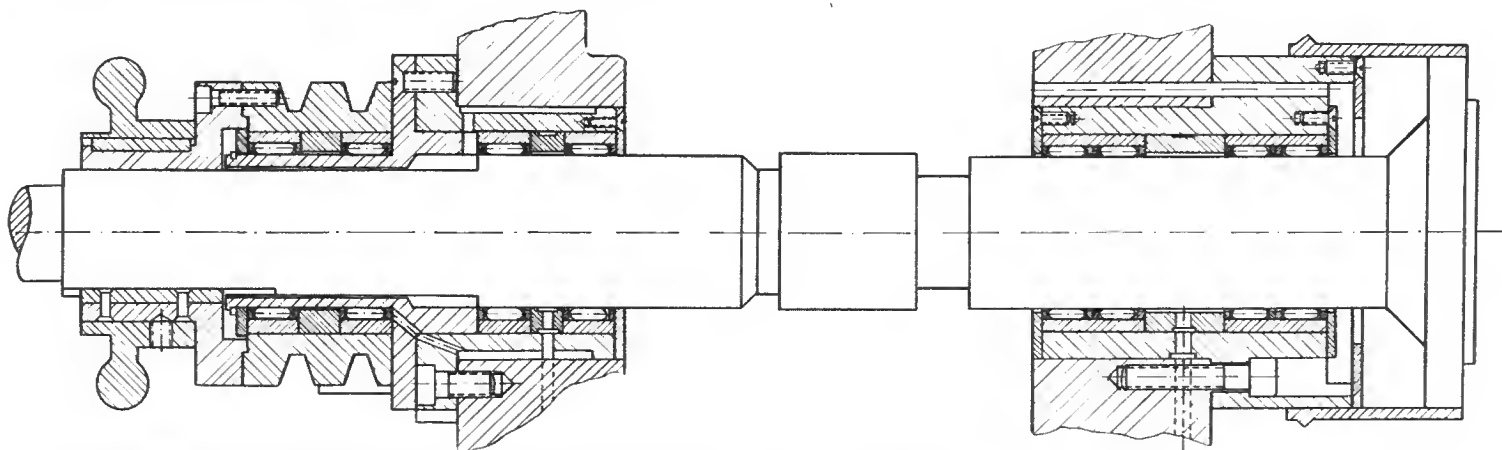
Werkstückspindellagerung einer Innenschleifmaschine mit Oszillereinrichtung (Hess. Werkzeug- und Apparatebau)
